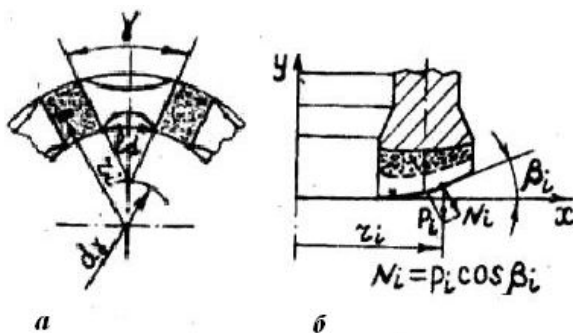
Схемы рабочего профиля коронки с плоской рабочей поверхностью (а) и с равноизносостойкой рабочей поверхностью (б)
